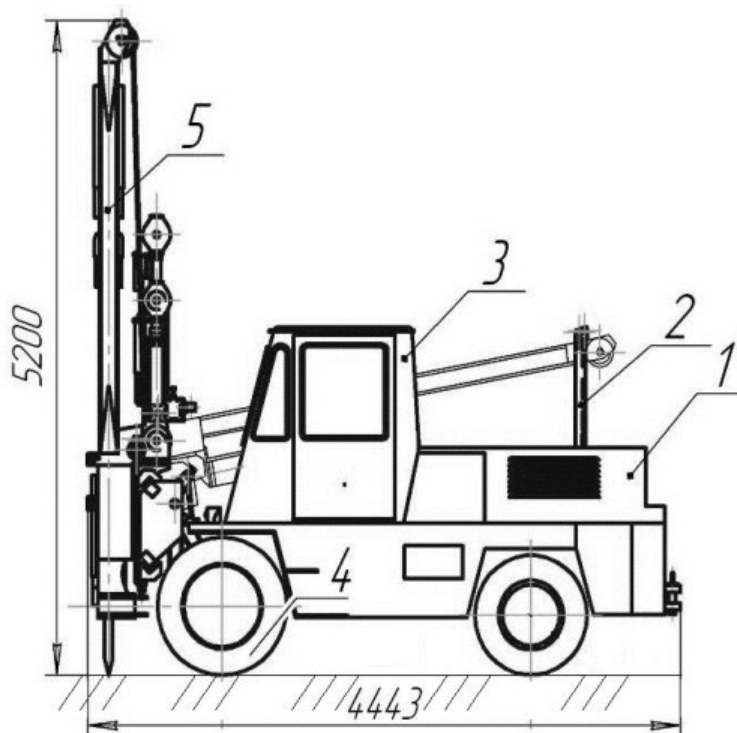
Общий вид машины для выполнения ремонтных, реконструкционных и дорожных работ на базе автопогрузчика: 1 - базовая машина; 2 - стойки; 3 - кабина; 4 - пневмоколесное ходовое оборудование; 5 - рабочее оборудование.
